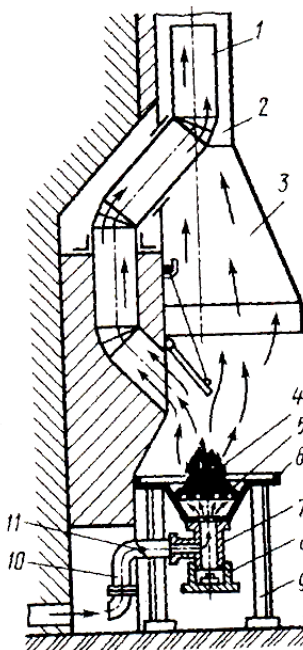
Стационарный горн из металла и кирпича: 1 – внутренняя труба; 2 – наружная труба; 3 – металлический зонт; 4 – уголь; 5 – колосниковая решетка; 6 – горновая чаша; 7 – фурма; 8 – крышка; 9 – подставка; 10 – воздухоподводящая труба; 11 – регулирующая заслонка
